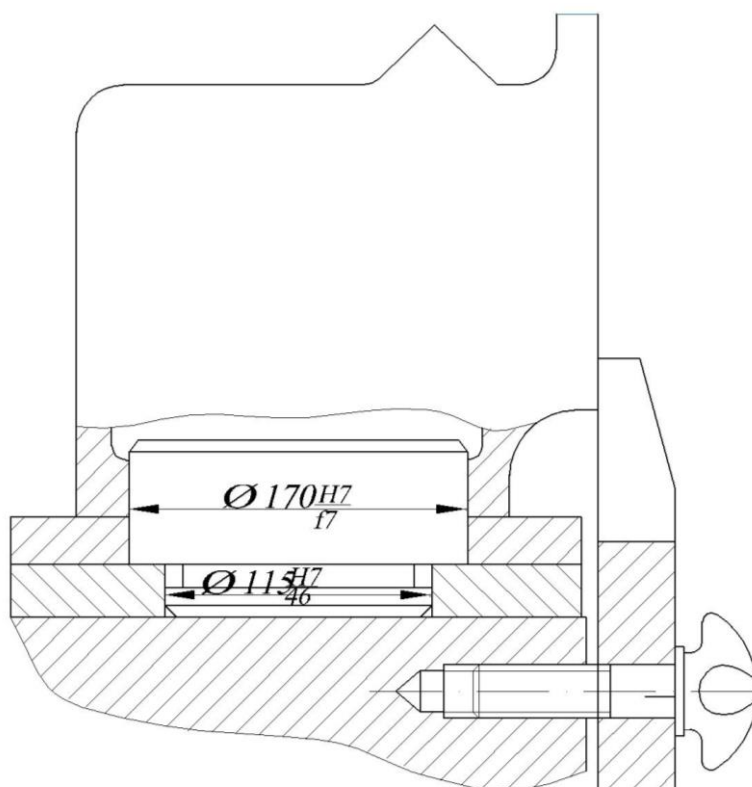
Схема установки деталі в агрегатне пристосування
